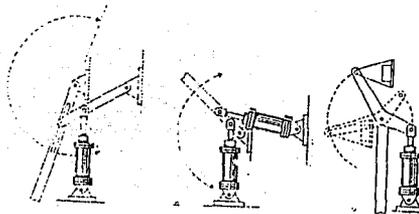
PRESA MOLDEADORA DE PLACAS DE HORMIGON.
